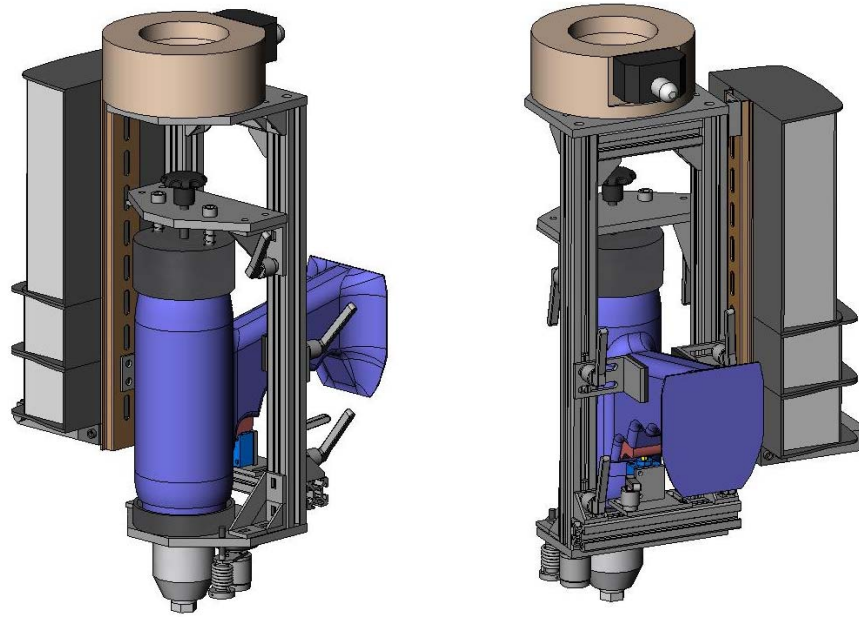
Bohrwerkzeug mit Schraubenspannung
